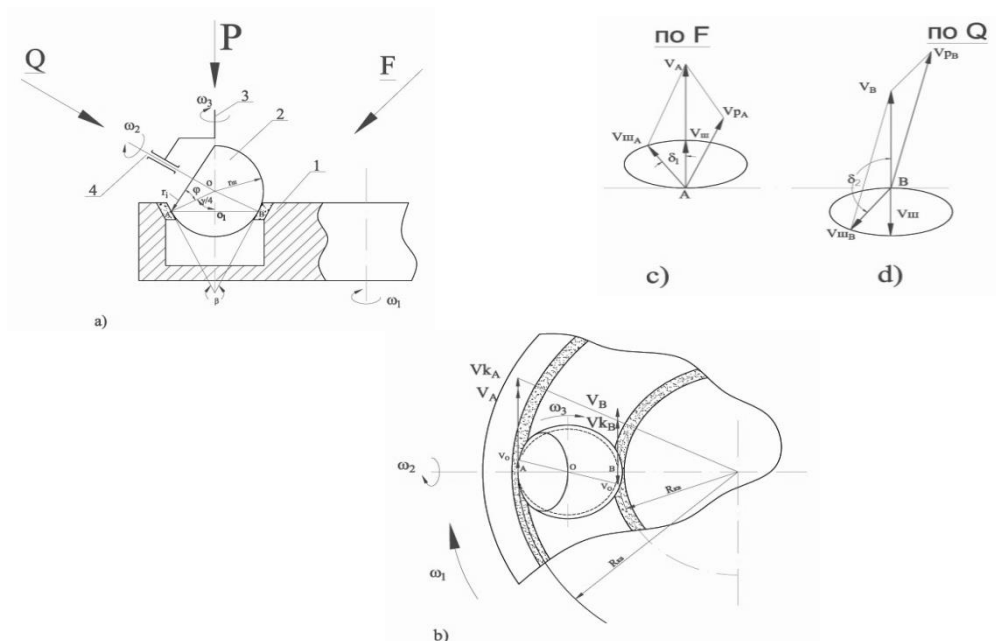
Кинематическая схема формообразования неполной сферической поверхности торцовым шлифованием на основе способа НППШ:
